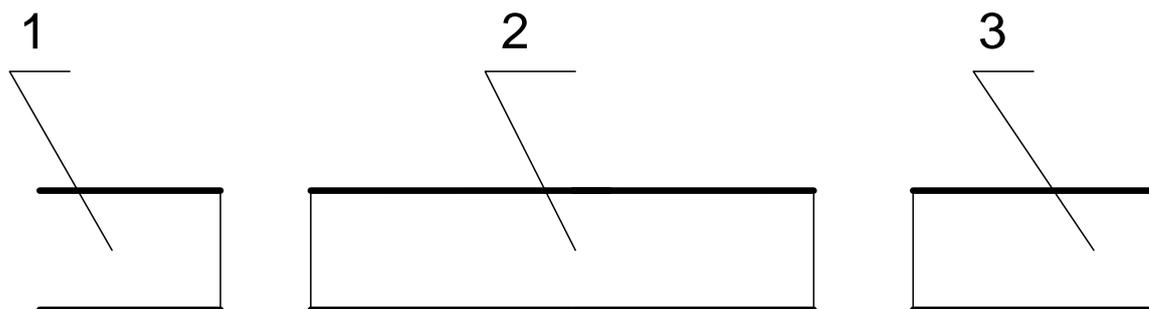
Конструкция контрольного сварного соединения
